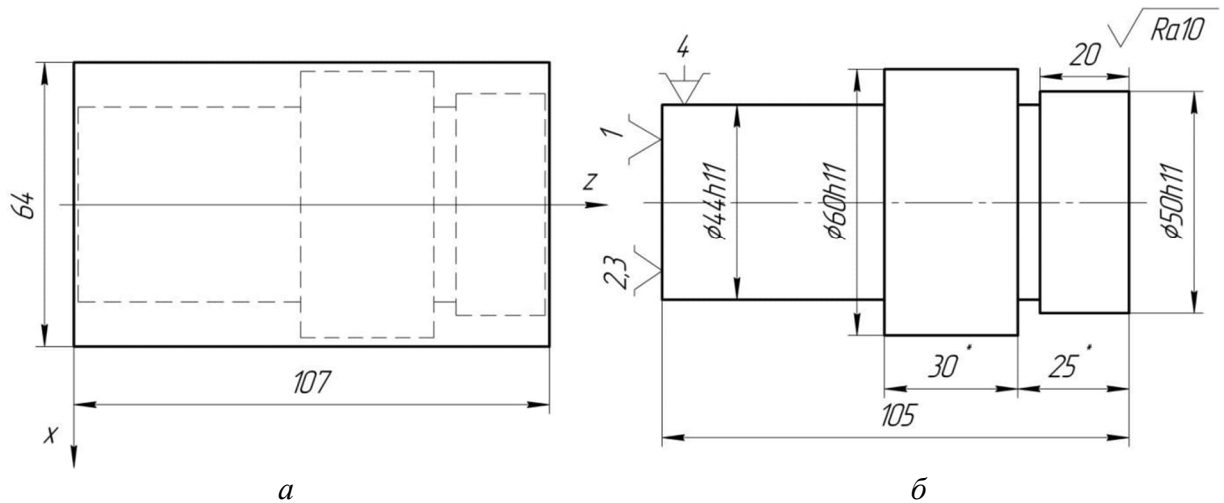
Вихідна заготовка (а) та деталь (б)
